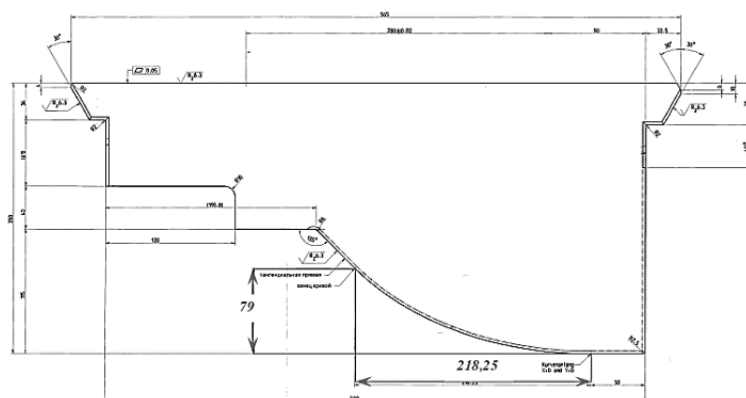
Верхний инструмент прессы подгибки кромок
